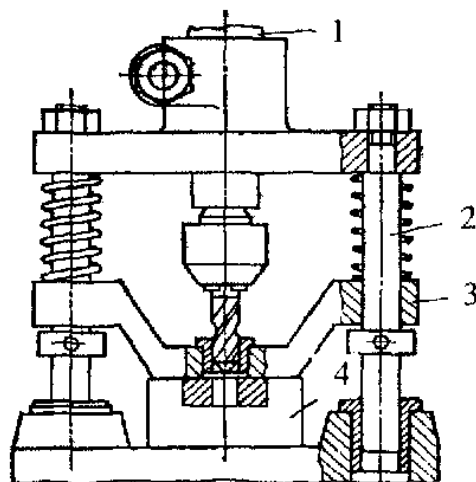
Схема автоматизованого пружинного затискача заготовки у свердлильному пристрої
